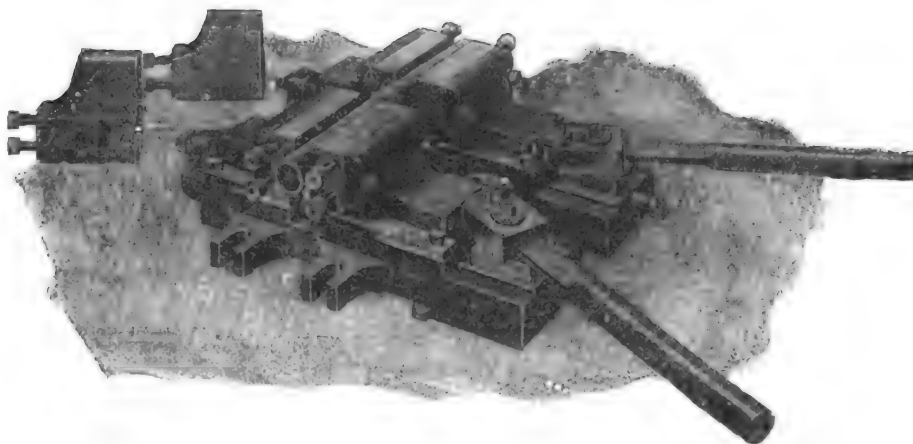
Pince pour la mise en place et la soudure de tubes.
